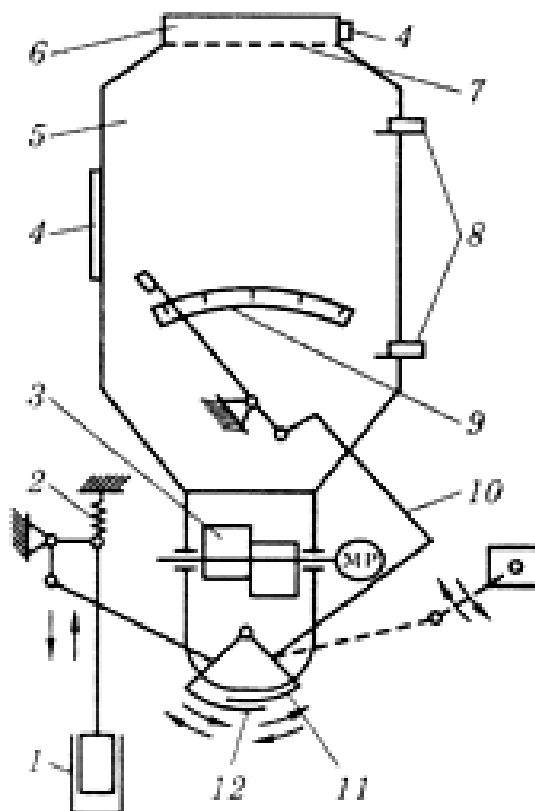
Конструкційна схема дозатора ДК-10: 1 – електромагніт; 2 – пружинка; 3 – зворушувач; 4 – фіксатор; 5 – бункер; 6 – горловина завантажувальна; 7 – сітка; 8 – давачі рівня; 9 – шкала; 10 – важільний механізм; 11 – заслінка регульовальна; 12 – заслінка приводна [1-5]
